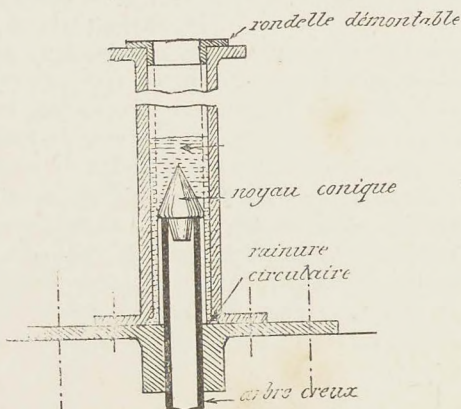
Partie supérieure de la machine à fabriquer les tuyaux.
